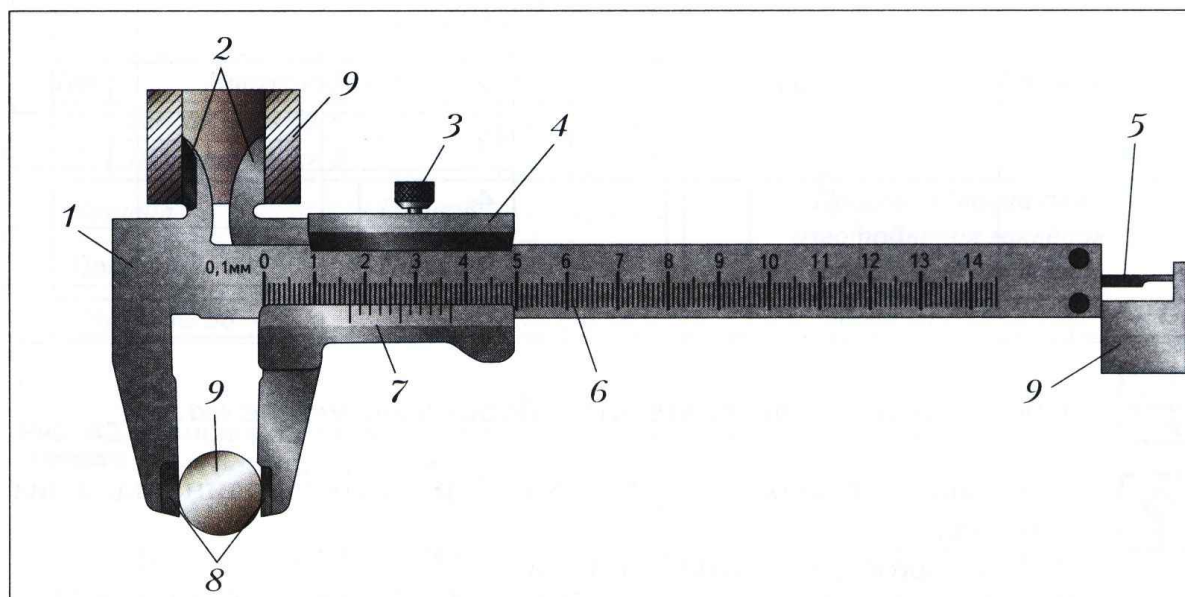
Штангенциркуль ШЦ-1: 1 — штанга; 2 — губки для внутренних измерений; 3 — зажимный винт для фиксации рамки; 4 — подвижная рамка; 5 — глубиномер; 6 — шкала штанги; 7 — нониус; 8 — губки для наружных измерений; 9 — измеряемые детали
